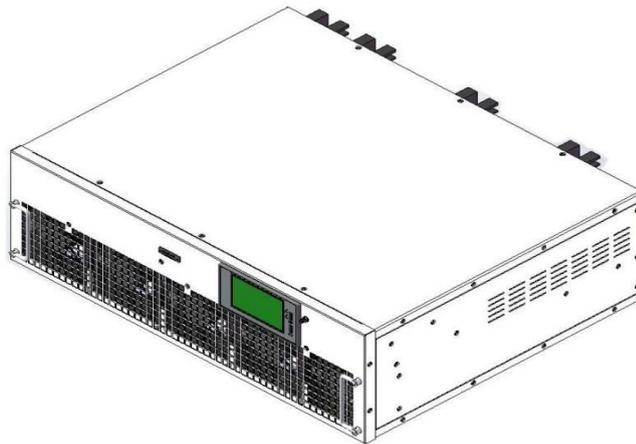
Forma de módulo tipo rack con 680 mm de ancho
